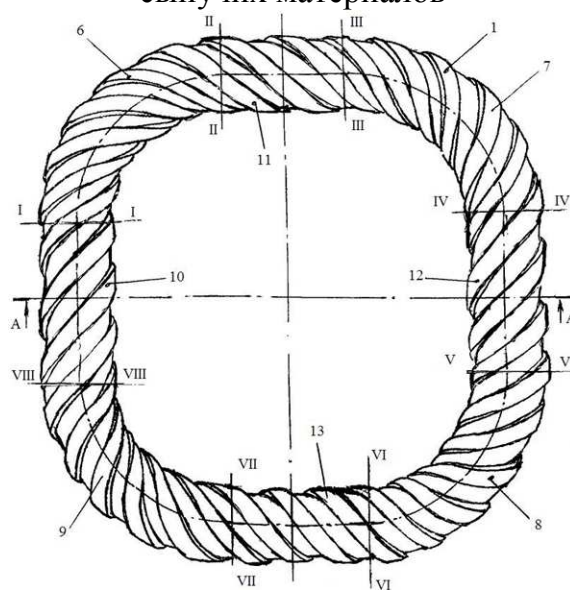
Изображение рабочей камеры 1, вид сверху
